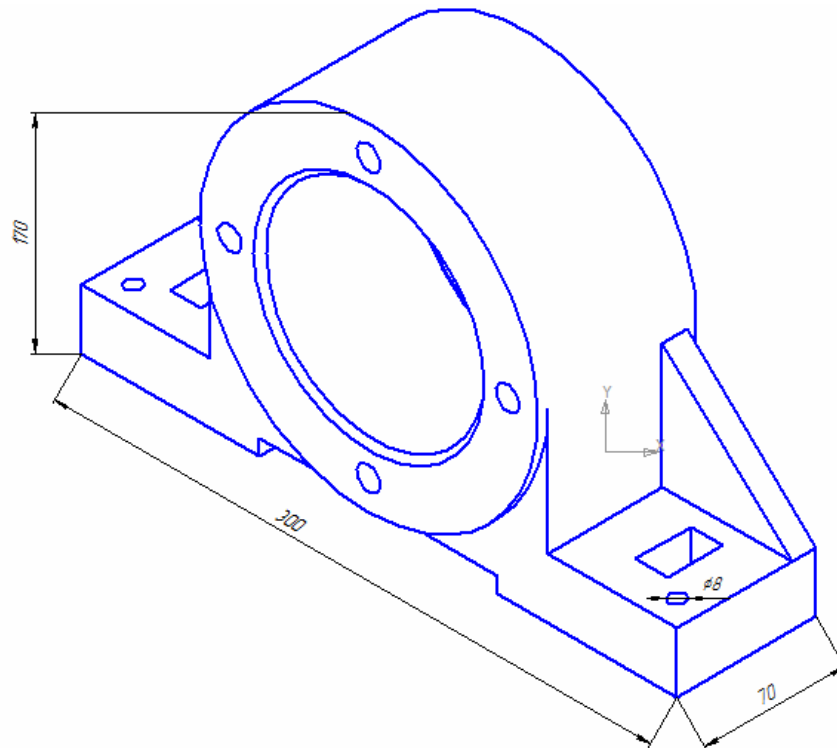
Аксонометрический чертеж детали «Корпус»
